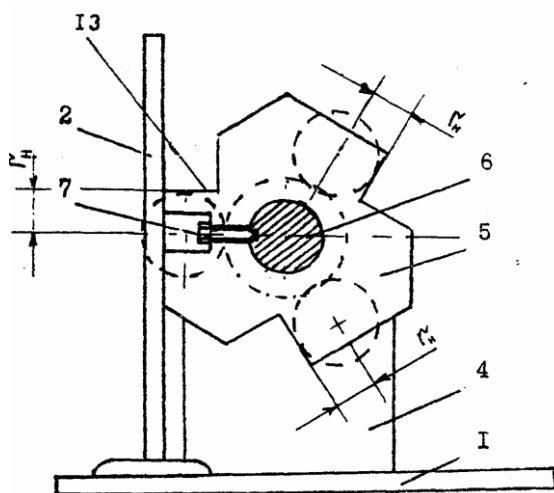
Устройство для измерения углового расположения шатунных шеек коленчатого вала под 120° . (вид сбоку)
